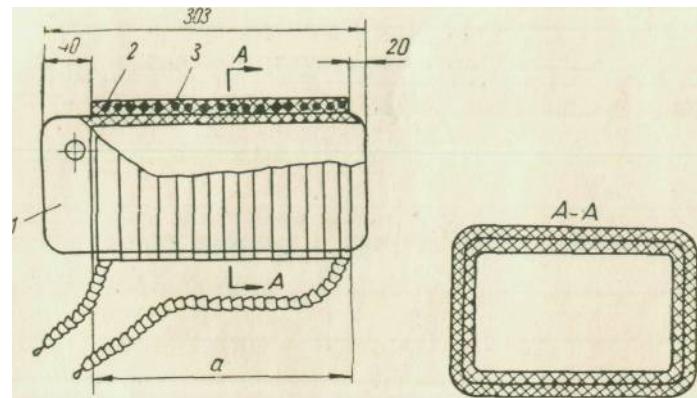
Узел нагревателя (гарнитурный чертеж):
